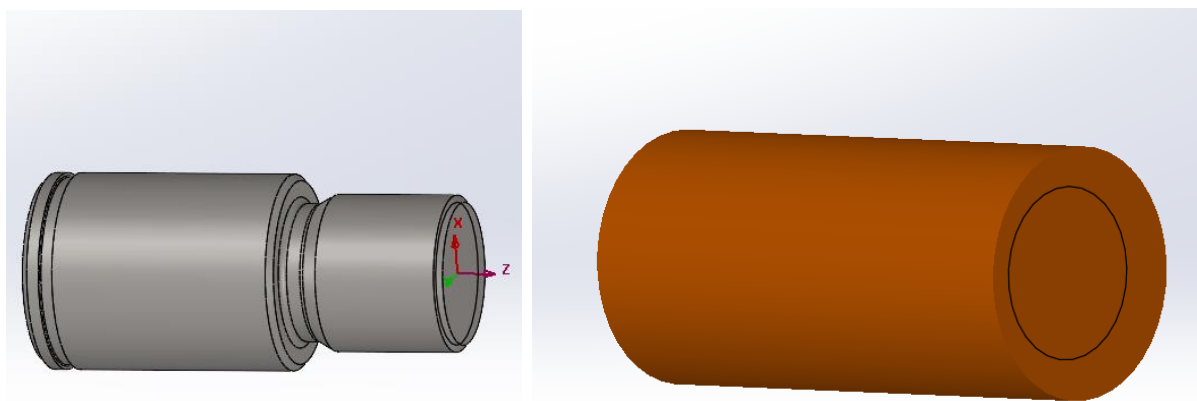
3D модель заготовки та деталі «Вал кріплення» (визначено масу – 0,44кг) (Деталь-0,31 кг)
